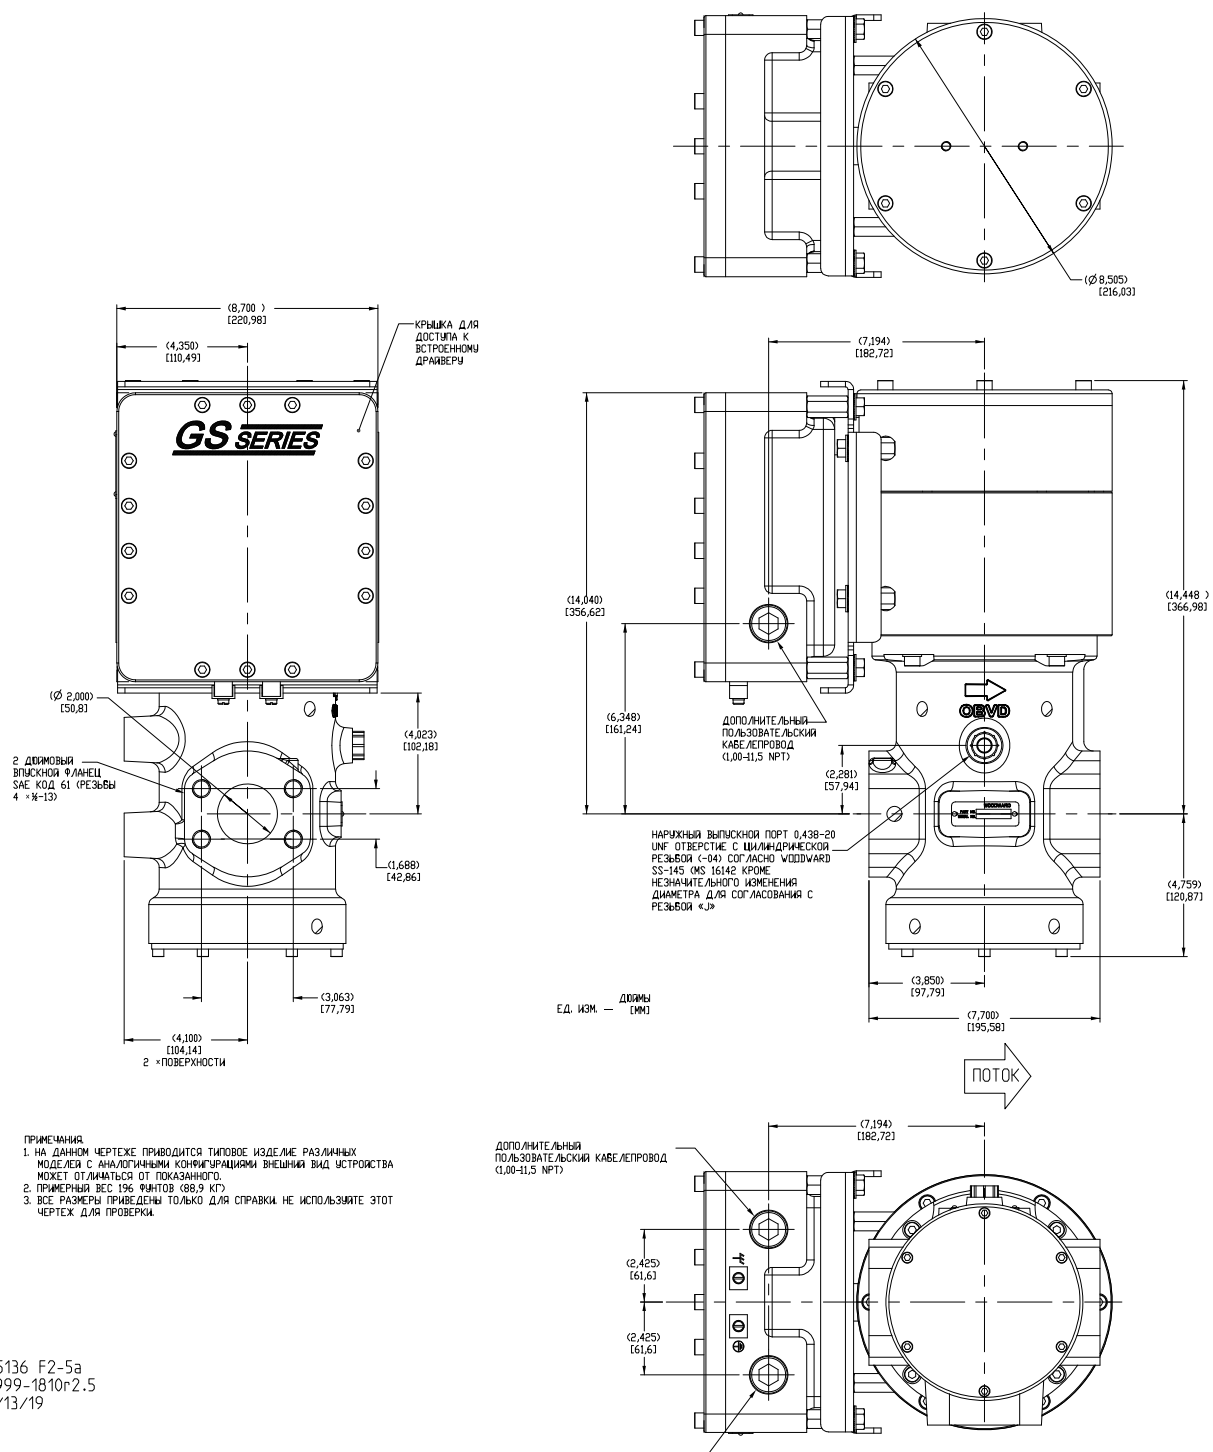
а. Габаритно-присоединительный чертеж, алюминий, GS50 с кабельными вводами
